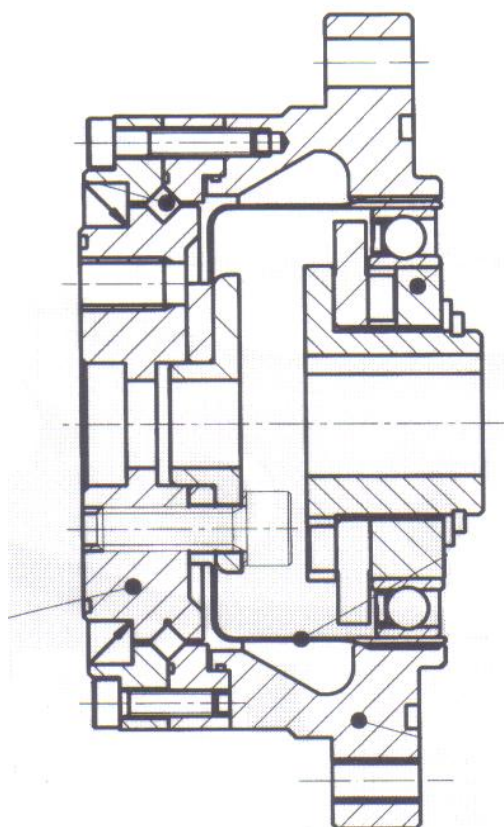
4 Současné provedení hrníčkové harmonické převodovky
